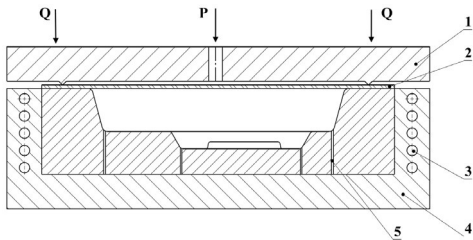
Штампы для ПТФ: 1 — прижим, 2 — заготовка, 3 — нагреватель, 4 — матрица, 5 — дренажное отверстие
